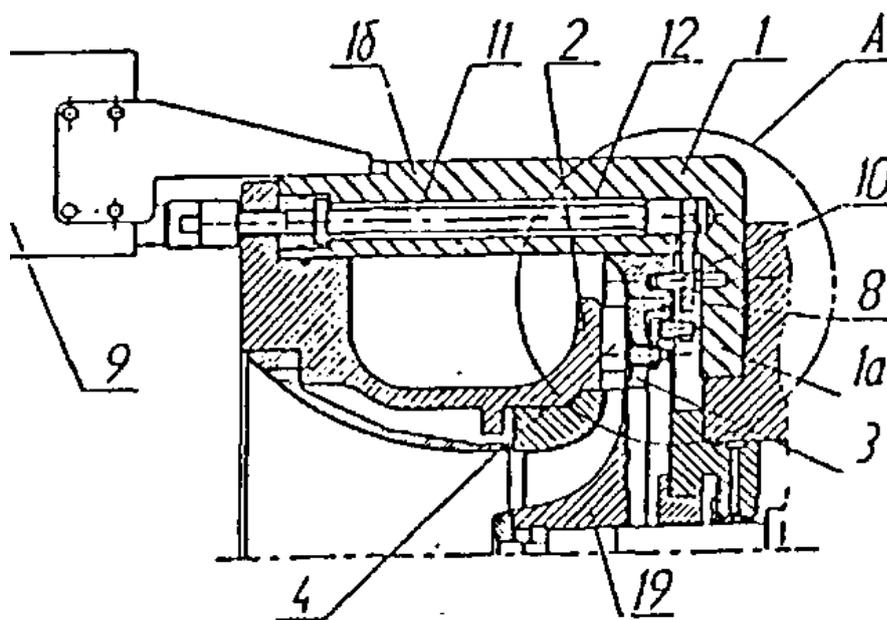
Регулируемый диффузор центробежного компрессора: 1 - корпус; 1 а - торцевая стенка корпуса 1; 1 б - обечайка корпуса; 2 - диафрагма; 3 - стенка диффузора; 4 - лопатки; 8 - приводной рычаг; 9 - привод; 10 - неподвижная ось; 11 - приводной вал; 12 - отверстие; 19 - рабочее колесо
